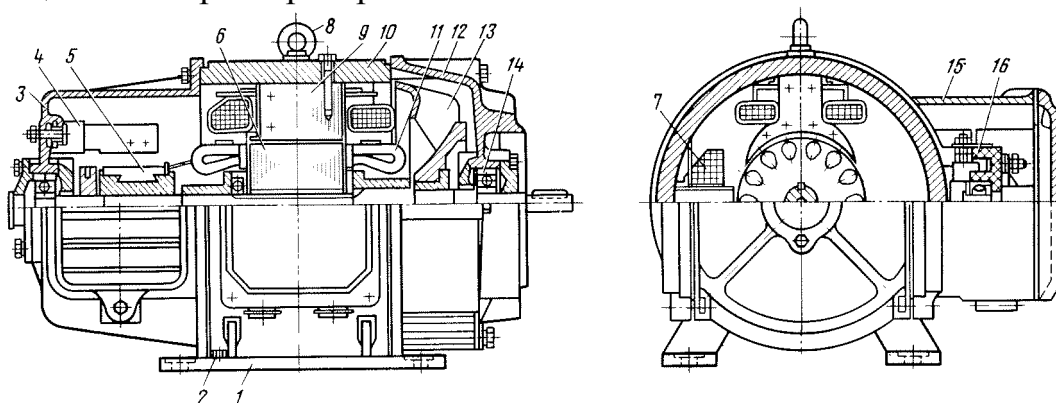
Электродвигатель типа П-31 вспомогательного компрессора
